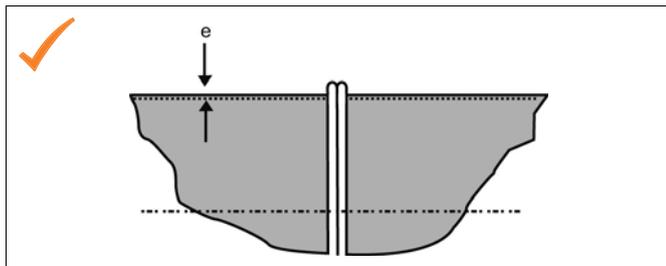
Schweißnaht mit gleichmäßiger Wulstausbildung (gut)
